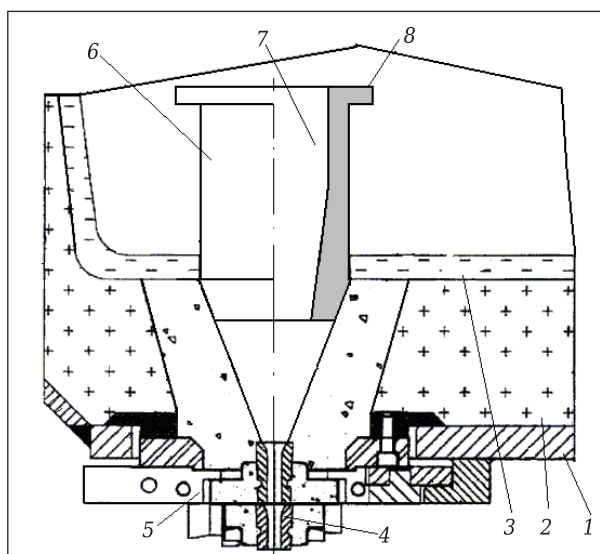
Компоновка оборудования разливочного отверстия ковша: 1 — корпус; 2 — огнеупорная футеровка; 3 — дно; 4 — стаканы-дозаторы; 5 — шиберный затвор; 6 — труба; 7 — конусообразная полость; 8 — кольцевой выступ трубы
